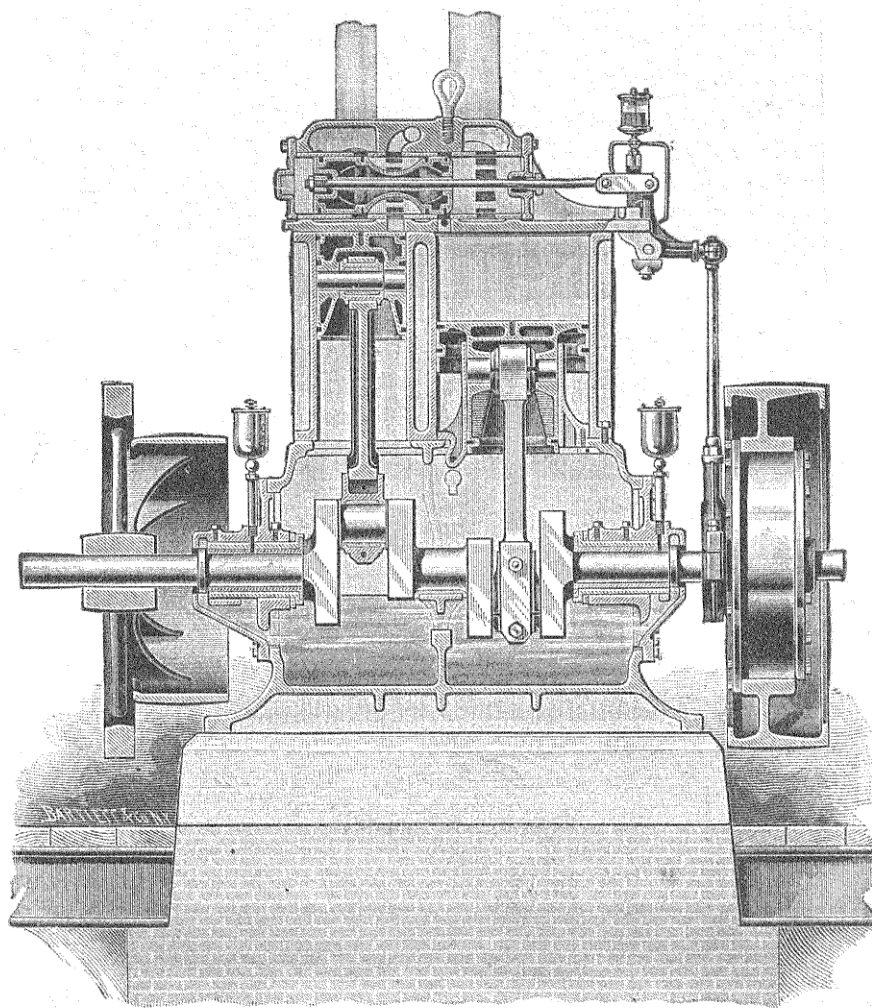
Coupe longitudinale d'une machine Westinghouse.
